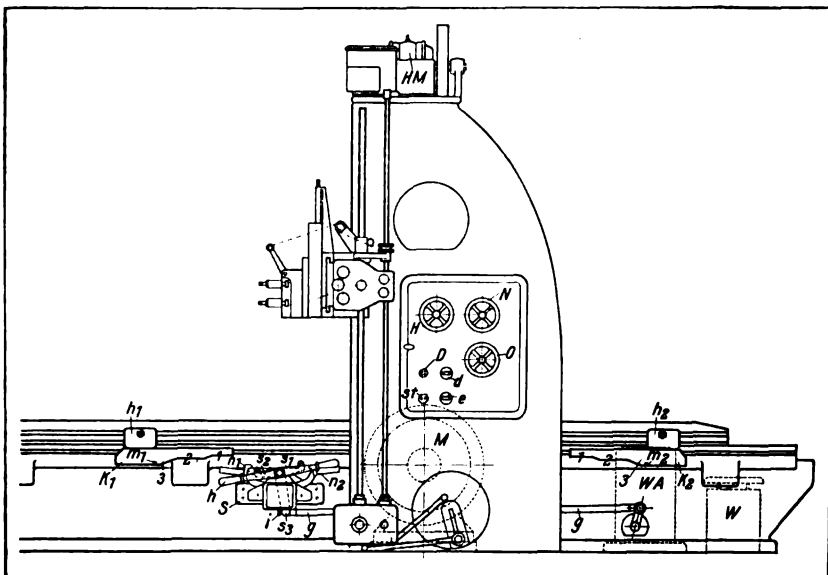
Umrißzeichnung einer Hobelmaschine mit elektrischem Antrieb durch Gleichstromwendemotor.
